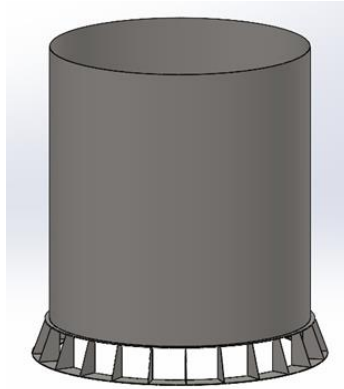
Encamisamento 8 mm sem vigas de suporte.
